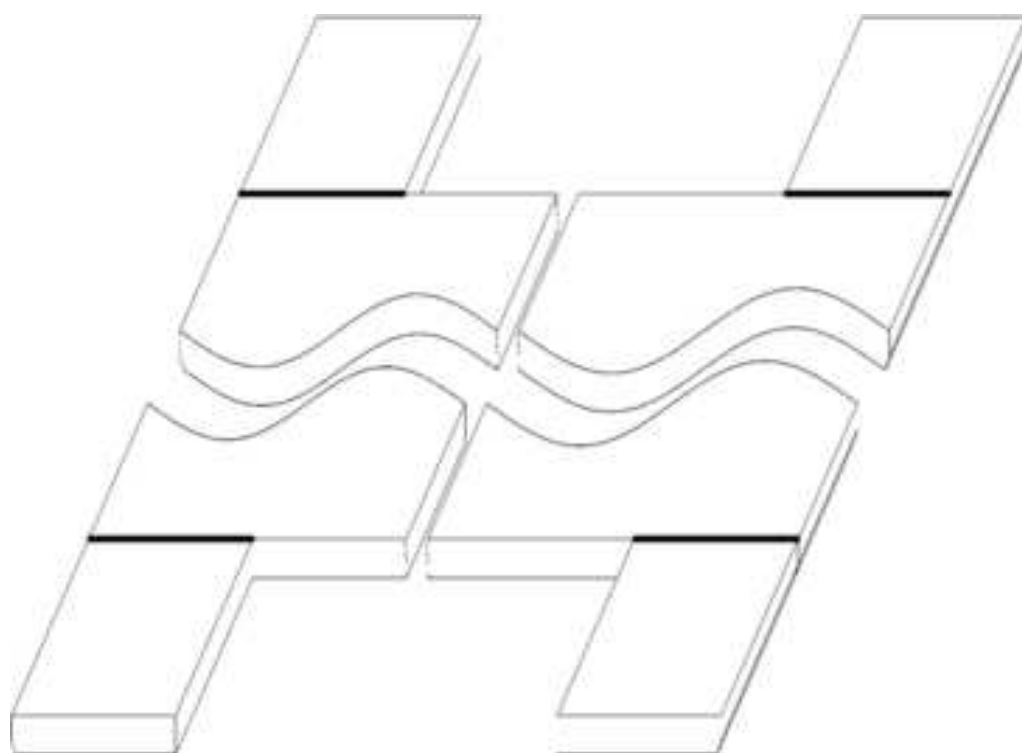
Лист с приваренными технологическими планками и подготовленный под сварку
